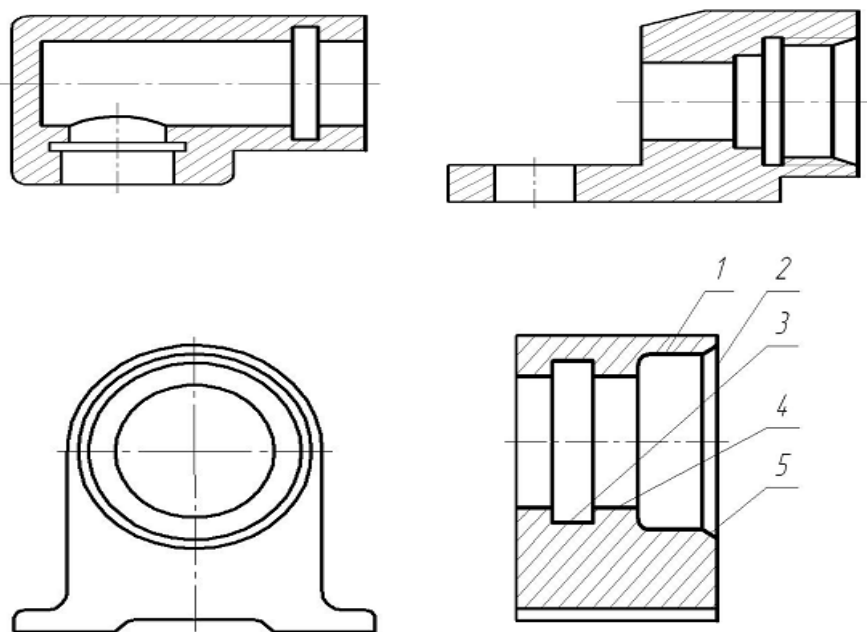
Група деталей для формування на основі комплексу ознак
